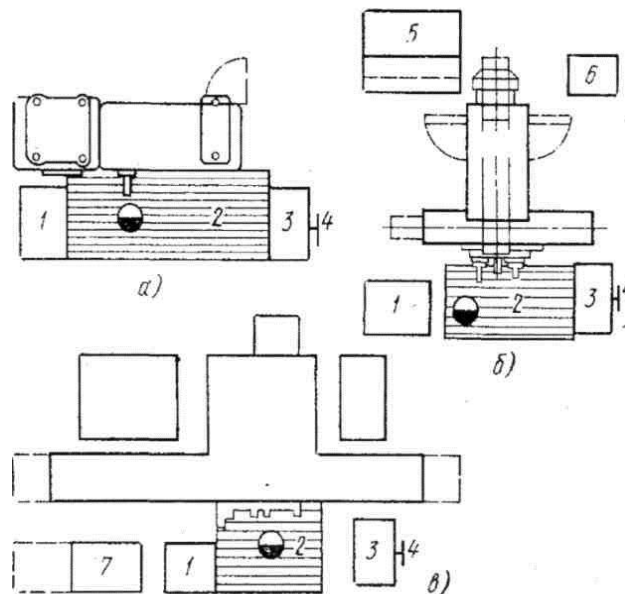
Планування робочих місць: а - токаря ; б - фрезерувальника ; в - шліфувальника ;
